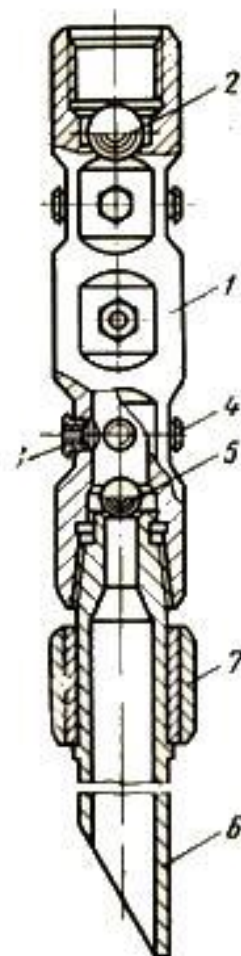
Аппарат для ГПП АП-6М: 1 - корпус; 2 - шар опрессовочного клапана; 3 - узел насадки; 4 - заглушка; 5 - шар клапана; 6 - хвостовик; 7 - центратор
